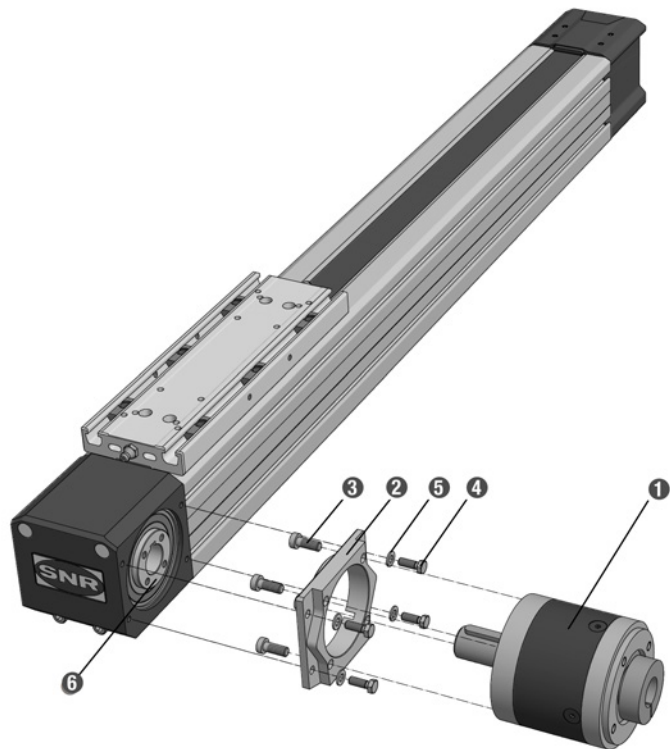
Formschlüssige Getriebemontage an Linearachsen mit Zahnriemenantrieb
